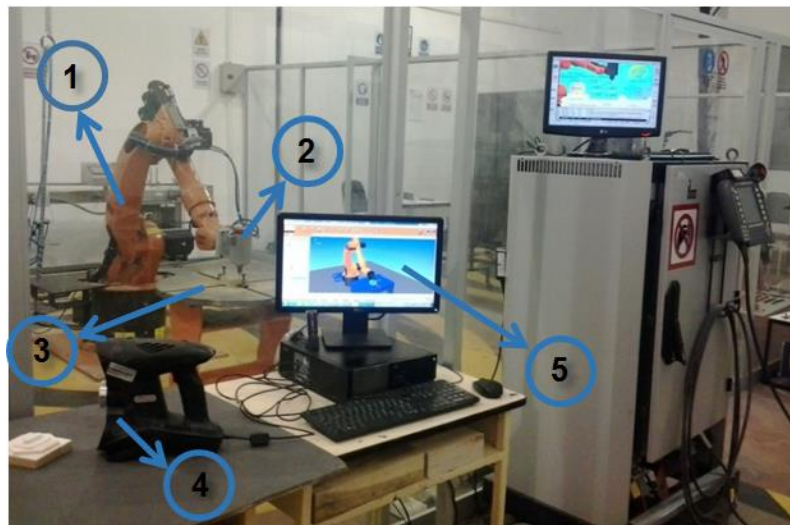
1: Celda de manufactura robotizada. Brazo robótico industrial KUKA KR16 (1). Cabezal fresador Jäger (2). Mesa de trabajo (3). Escáner 3D (4). PC (5).
